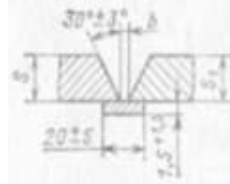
Подготовка кромок труб с подкладными кольцами к сварке
